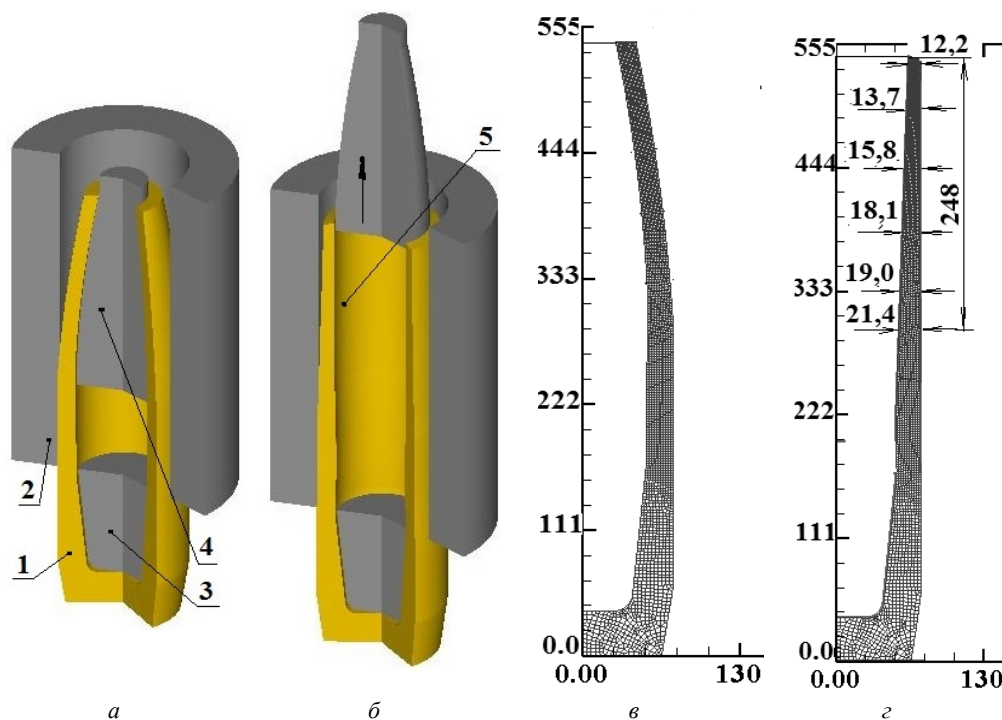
Розрахункові схеми для визначення форми і розмірів заготовки для обтиску: *a* – схема перед вирівнюванням стінки, *б* – схема після вирівнювання стінки, *в* – половина заготовки з розмірами по ескізу, *г* – заготовка після вирівнювання
